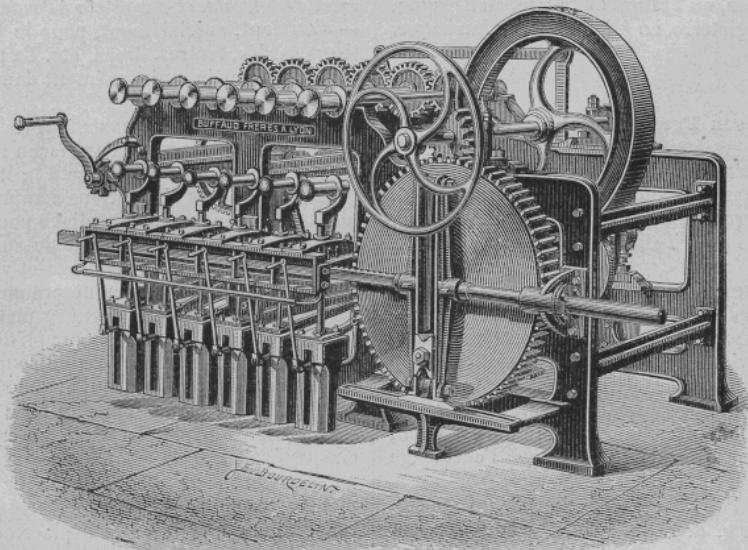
Machine à cheviller les soies (construction Buffaud et Robatel).
